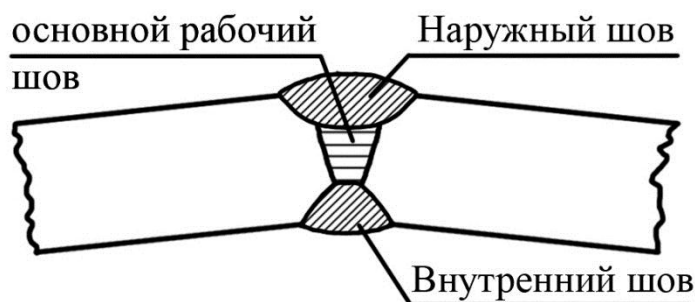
Схема швов, выполненных в предлагаемом способе сварки
